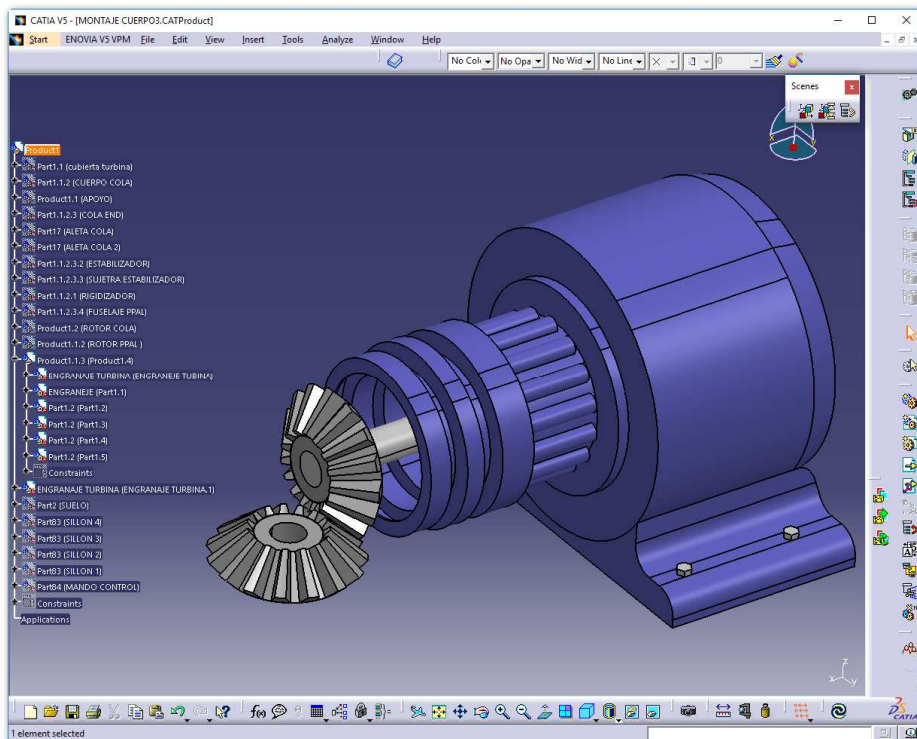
Conjunto del mecanismo de transmisión del rotor principal.
